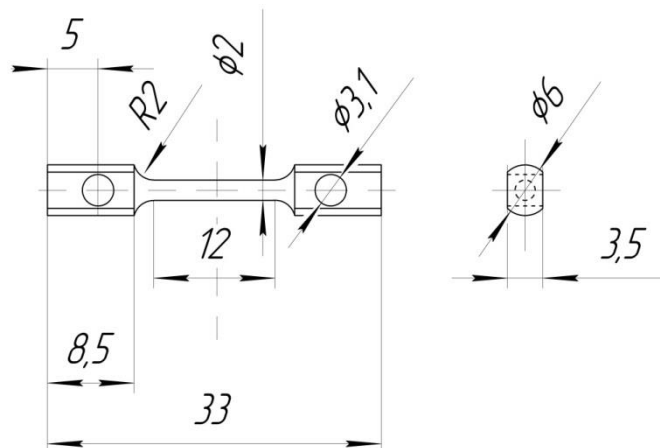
Образец для автоклавных испытаний на коррозионное растрескивание под напряжением из стали 304L и 316CW
